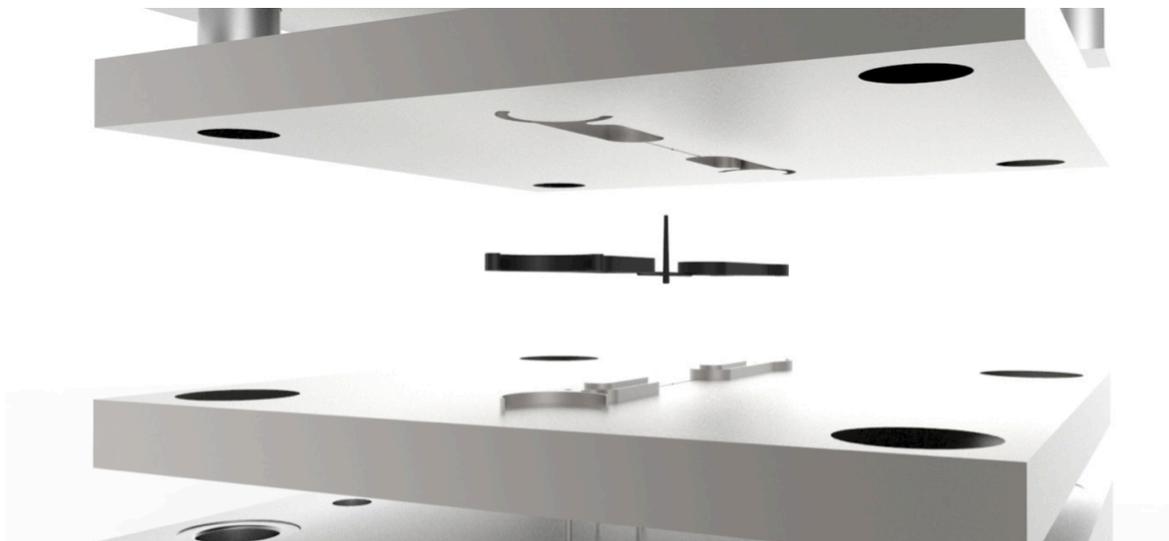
Acercamiento de las cavidades del molde con pieza inyectada
